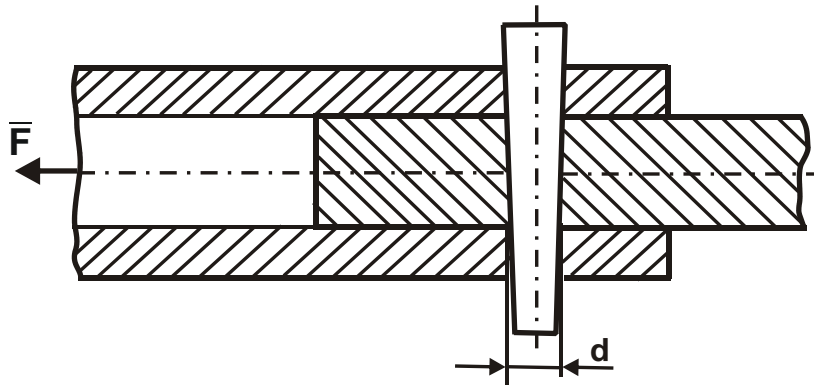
Розрахункова схема штифтового з'єднання
